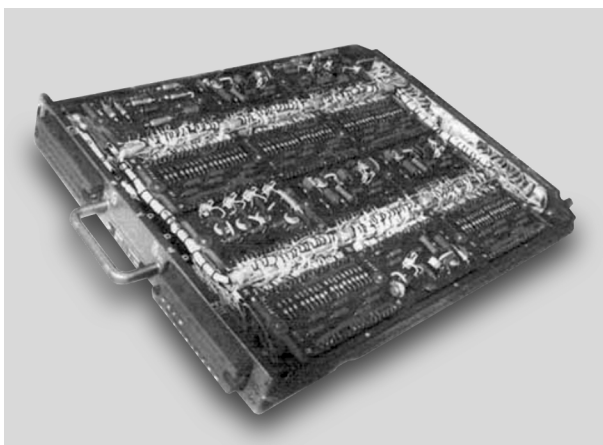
Типовая конструкция блока ЭВМ М4-2М.
